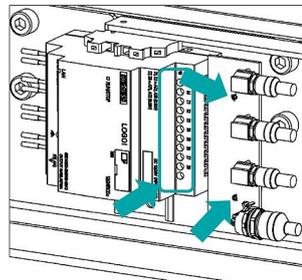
, Steuerung: Verschraubung Platine lösen/befestigen
